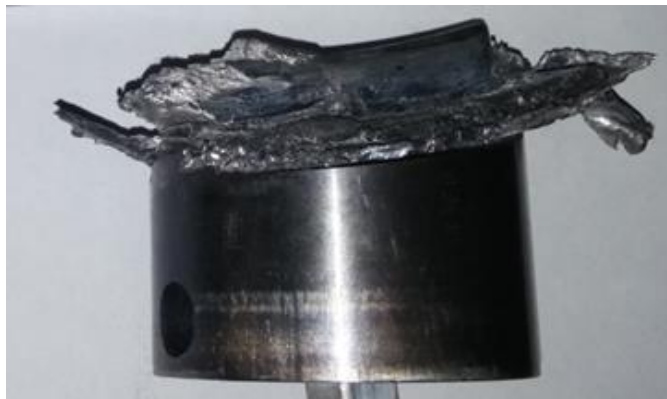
Общий вид профиля гравюры рабочего колеса варианта оснастки №2
